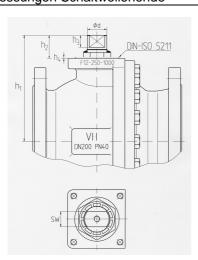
Kugelhahn mit vollem Durchgang und Flanschanschluß nach DIN EN 1092-1, Form B1 (DIN 2526 Form C); Baulänge: Grundreihe 27 nach EN 558-1 (F18 nach DIN 3202 Teil 1)
